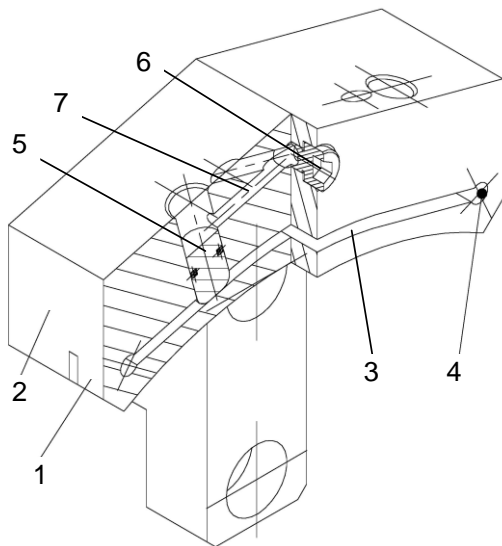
Затискний кулачок з пружними компенсаційними ланками для затиску тонкостінних деталей з циліндричними базовими поверхнями
